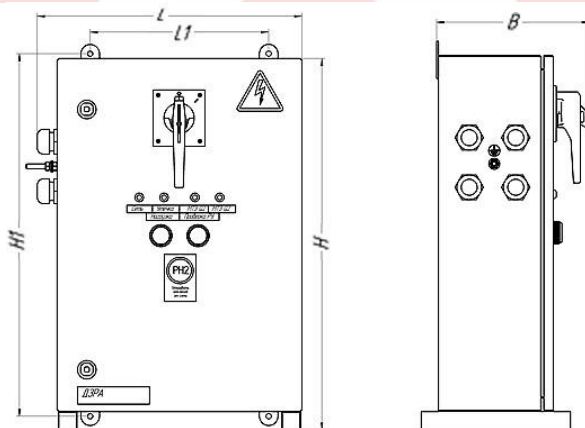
Общий вид, габаритные и установочные размеры АОШ-Х-Х-127В/220В (1,6-10 кВА)
